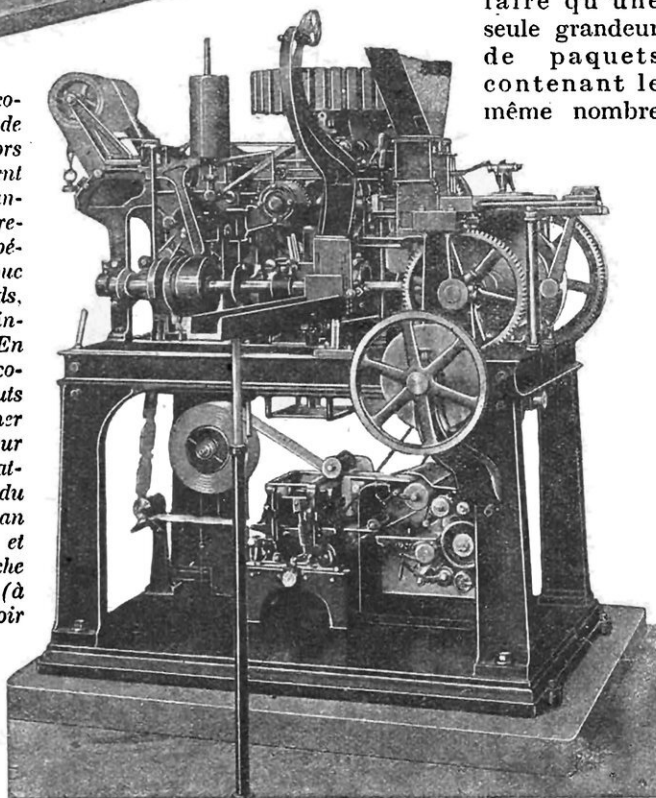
MACHINE BOULIET, ÉGALEMENT DESTINÉE
